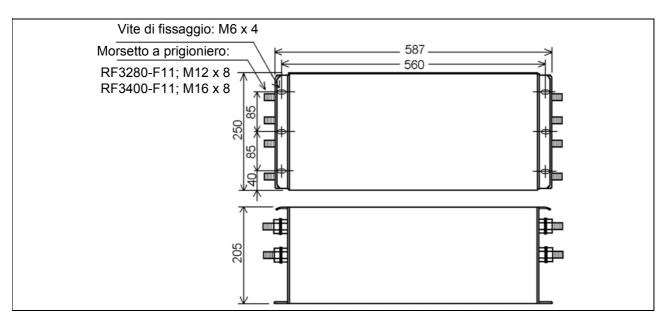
Dimensioni filtri (RF3280-F11, RF3400-F11)
